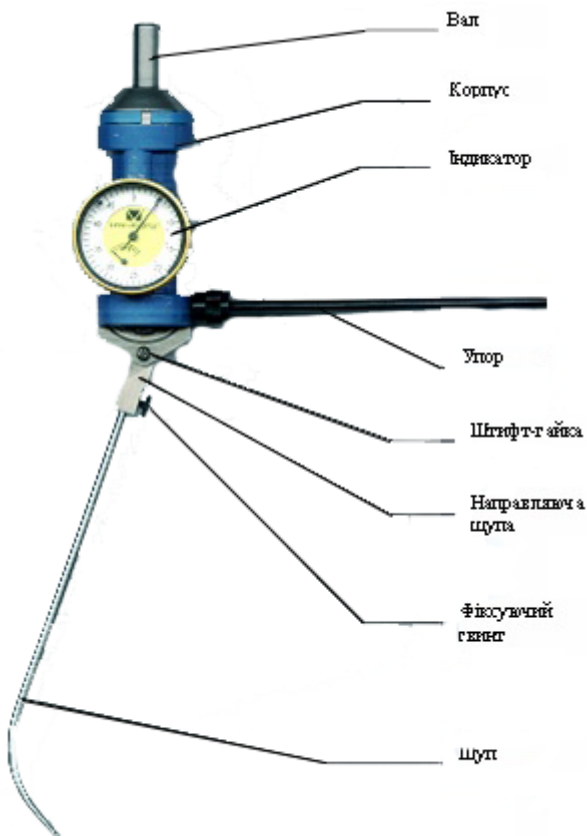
Центрошукач індикаторний ЦИ-03-0,01
